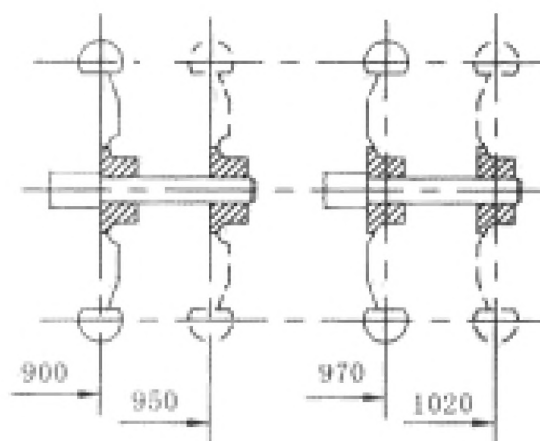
Бесступенчатая регулировка ширины колес задних колес.
